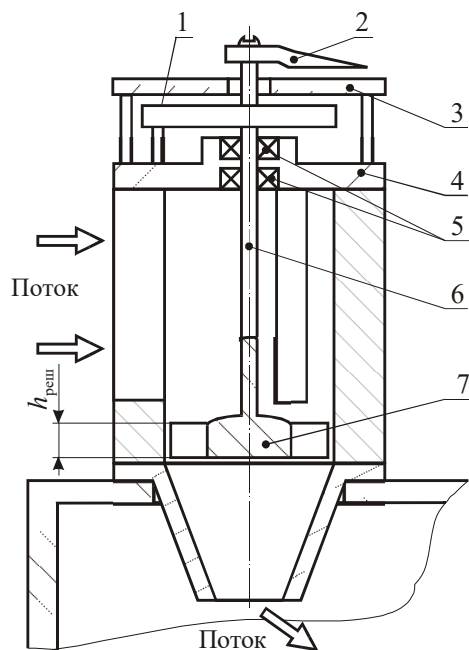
Конструктивная схема устройства для измерения момента количества движения потока: 1 – спиральная пружина; 2 – стрелка прибора; 3 – диск со шкалой; 4 – торцевая крышка; 5 – малогабаритные подшипники; 6 – ось; 7 – диск с лопастями (спрямляющая решетка)
